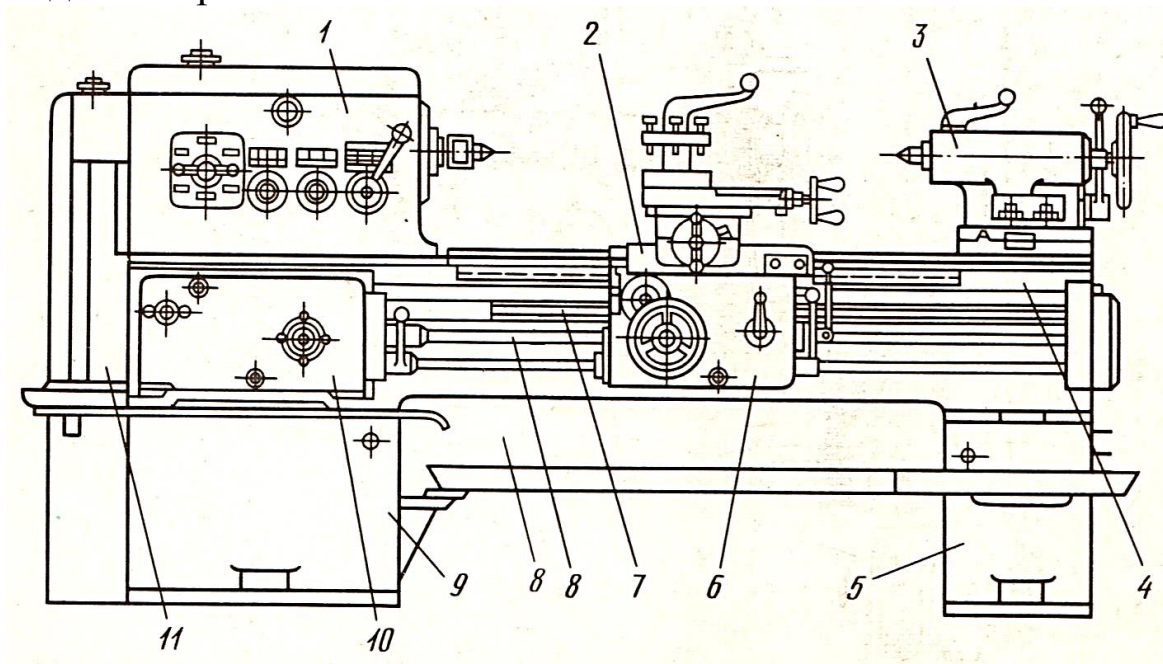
Устройство токарно-винторезного станка: 1 – передняя бабка; 2 – суппорт; 3 – задняя бабка; 4 – станина; 5 и 9 – правая и левая тумбы; 6 – фартук; 7 – ходовой винт; 8 – ходовой валик; 10 – коробка подач; 11 – гитара сменных зубчатых колёс
